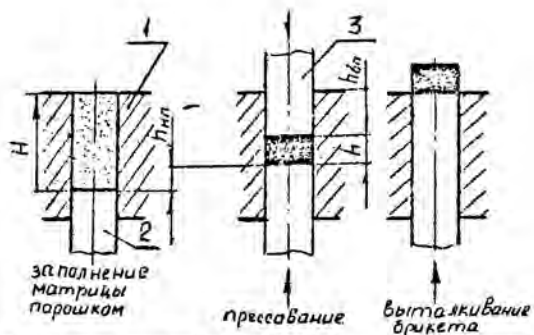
Схема прессформы с неподвижной матрицей для двустороннего прессования:
